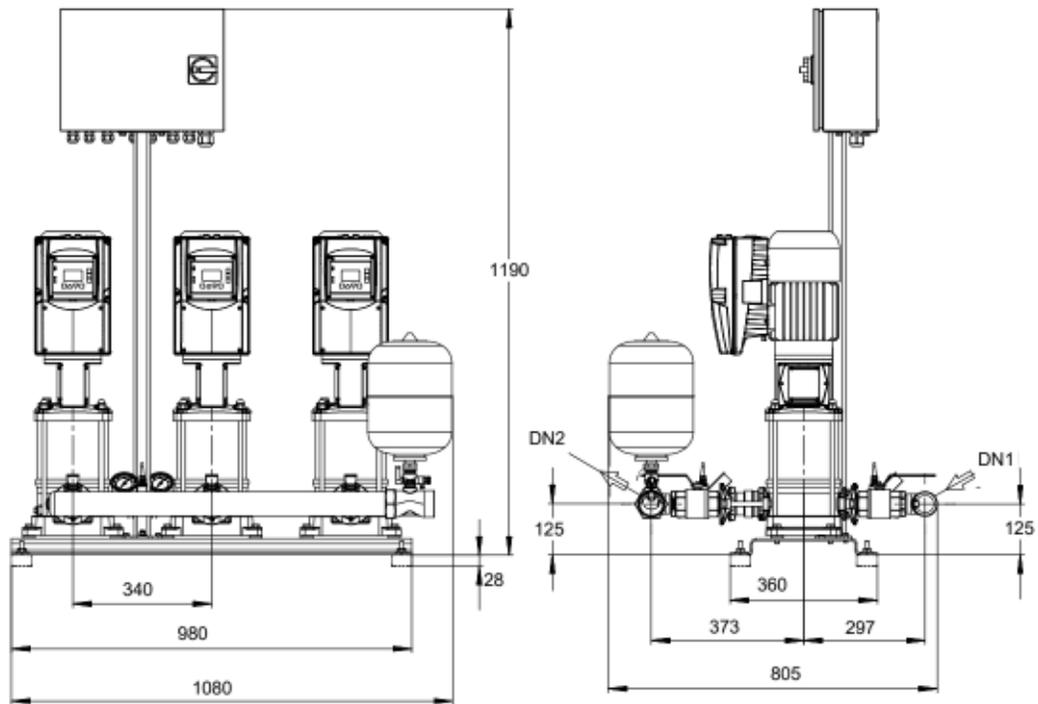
Perfiles con dimensiones del equipo presurizador Delta Basic.
